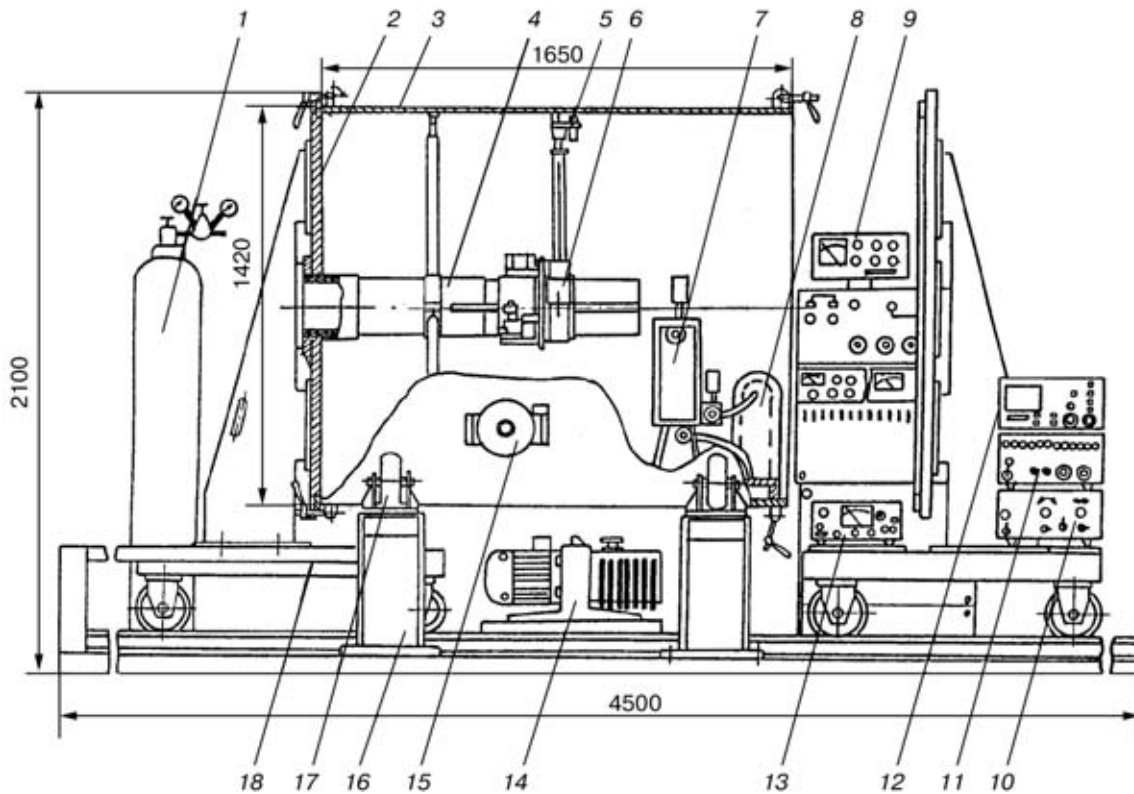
Лабораторный стенд Об-2266 для испытания методов и средств контроля герметичности сварных соединений многослойных труб большого диаметра и других крупногабаритных изделий (обозначения см. в тексте)
